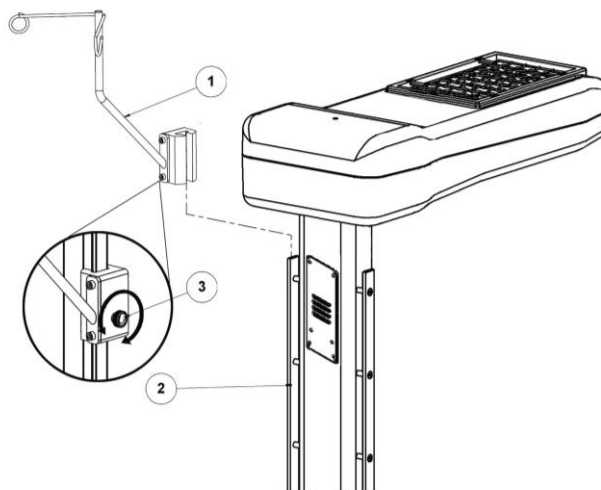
Montagem do Suporte de Soro Menor Móvel
